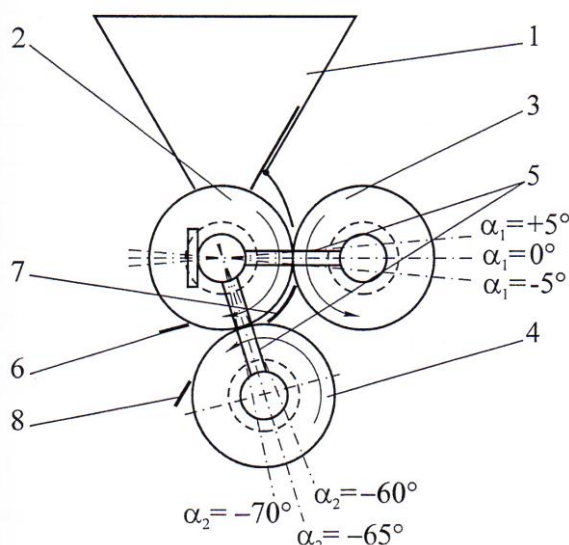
Схема установки бокового и нижнего валцов: 1 – питательный бункер с регулировочной заслонкой и направляющей криволинейной пластиной (ускорителем); 2 – верхний основной валец; 3 – боковой валец; 4 – нижний валец; 5 – регулировочный механизм межвальцового зазора; 6, 8 – очищающий нож; 7 – направляющая криволинейная пластина
